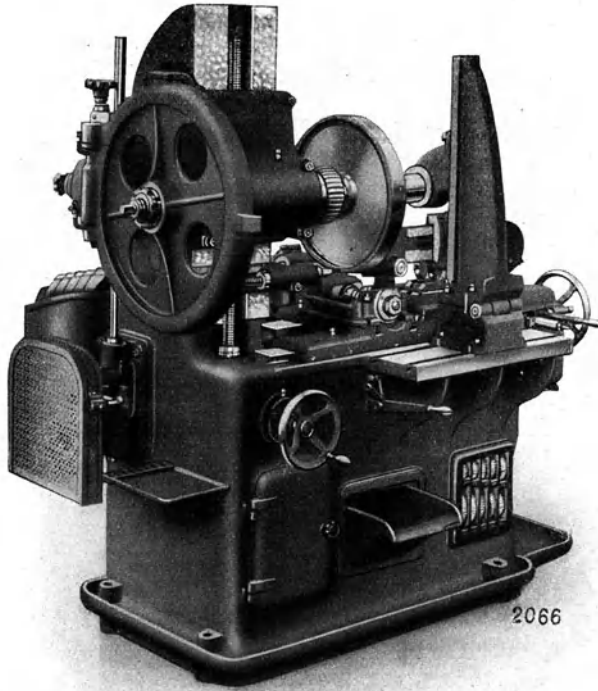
Die selbsttätige Stirnräderfräsmaschine von J. E. Reinecker.
